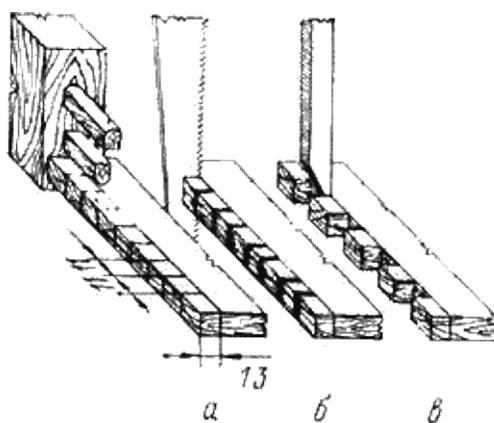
Подготовка ящичной вязки: а — разметка рейсмусом; б — зашлифовывание шипов; в — выдалбливание проушин
